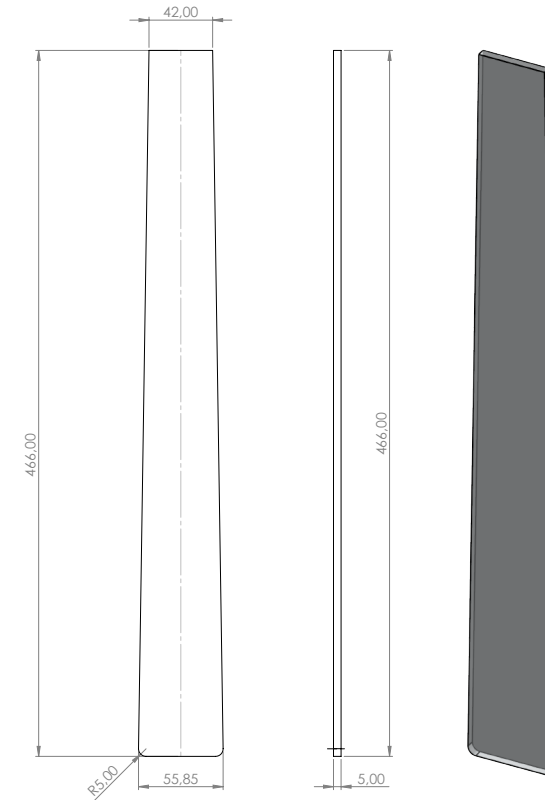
Desenho técnico e modelo 3D - Fretboard de vidro para maquete.
